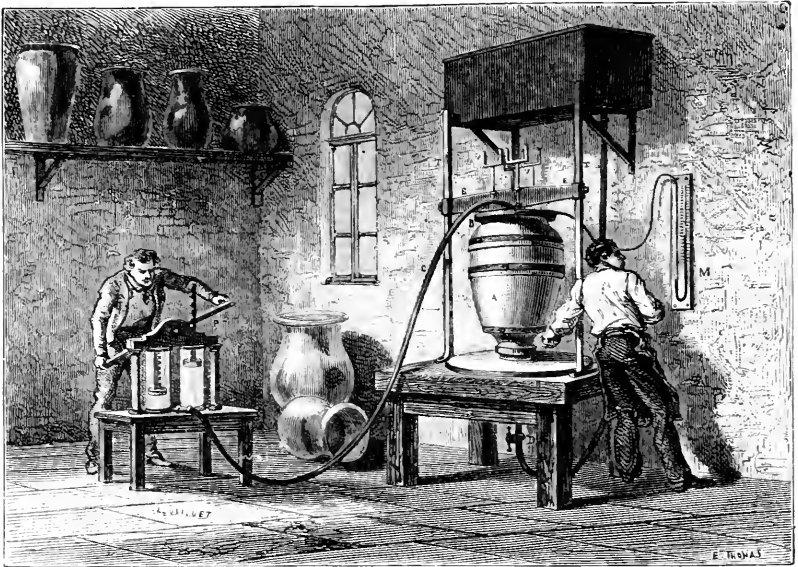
Appareil employé à la manufacture de Sèvres pour façonner les grandes pièces par le procédé du coulage avec le secours de l'air comprimé agissant à l'intérieur du moule.
